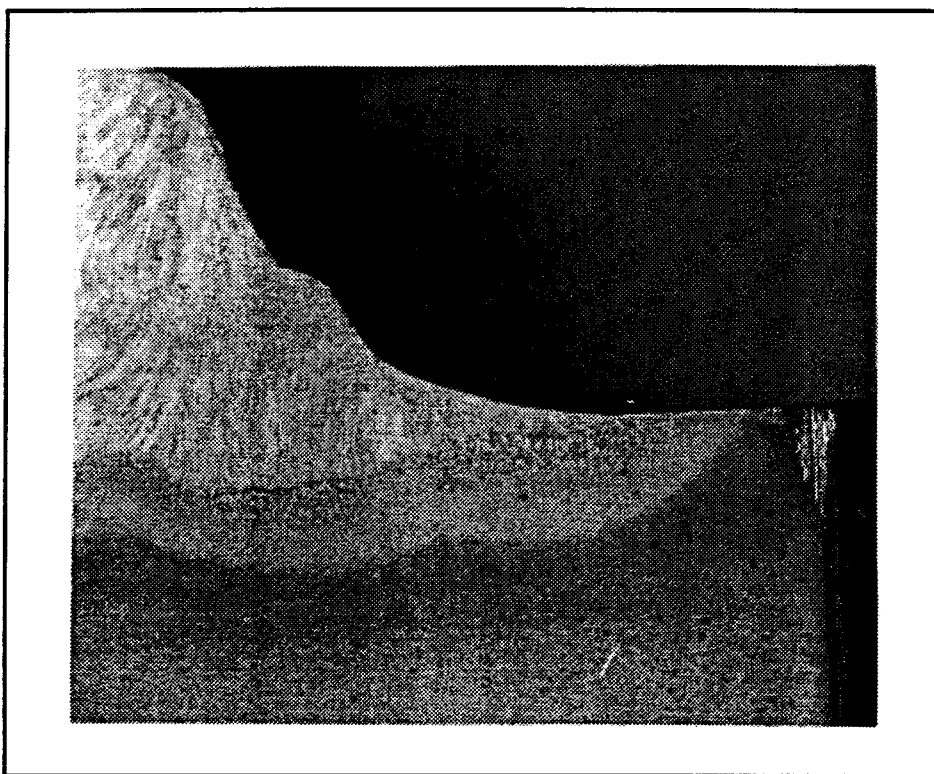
Pied de cordon de soudure refondu à la torche TIG (attaque nital 0,2 %)
